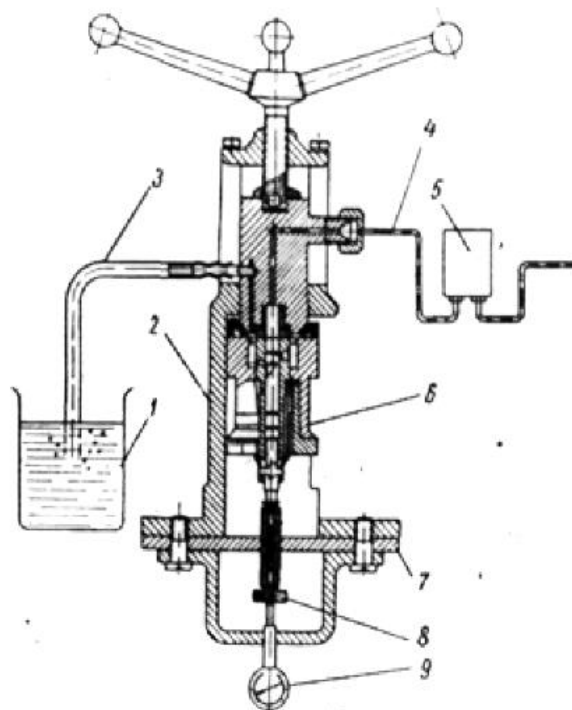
Принципова схема приладу для вимірювання активного ходу плунжера: 1 — скляна посудина; 2 — корпус приладу; 3 — поліетиленова трубка; 4 — трубка подачі повітря; 5 — редуктор тиску; 6 — знімна чашка; 7 — дошка; 8 — гвинт; 9 — індикатор тактового типу
